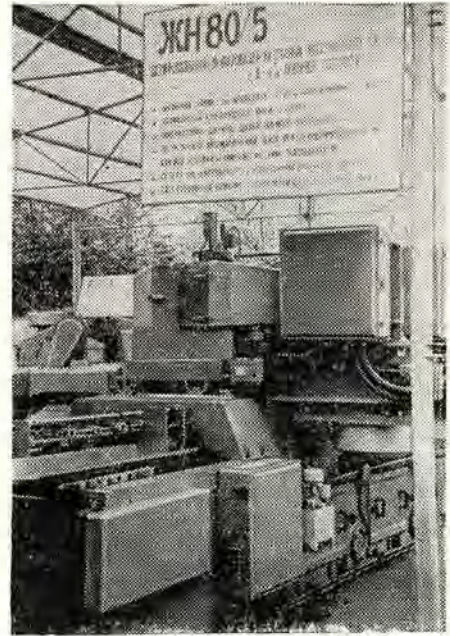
Шлифовально-полировальный станок для обработки мрамора.
